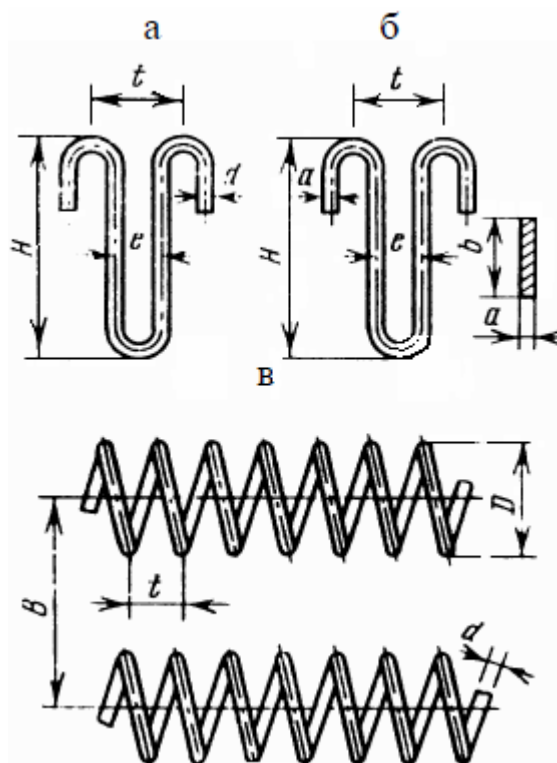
Эскизы проволочных и ленточных нагревателей: а – проволочный зигзагообразный, б – то же ленточный, в – спиральный
